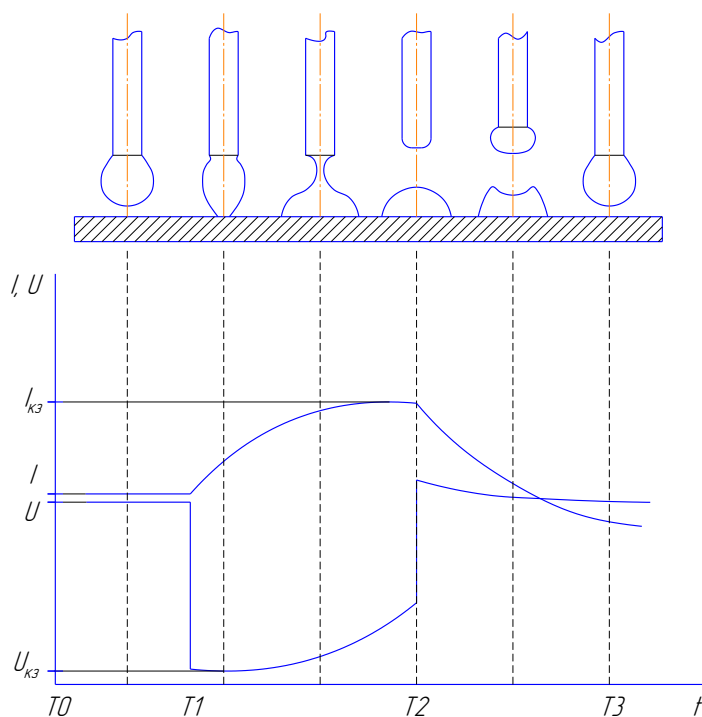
Типичные формы кривых сварочного тока и напряжения при традиционном способе полуавтоматической сварки
